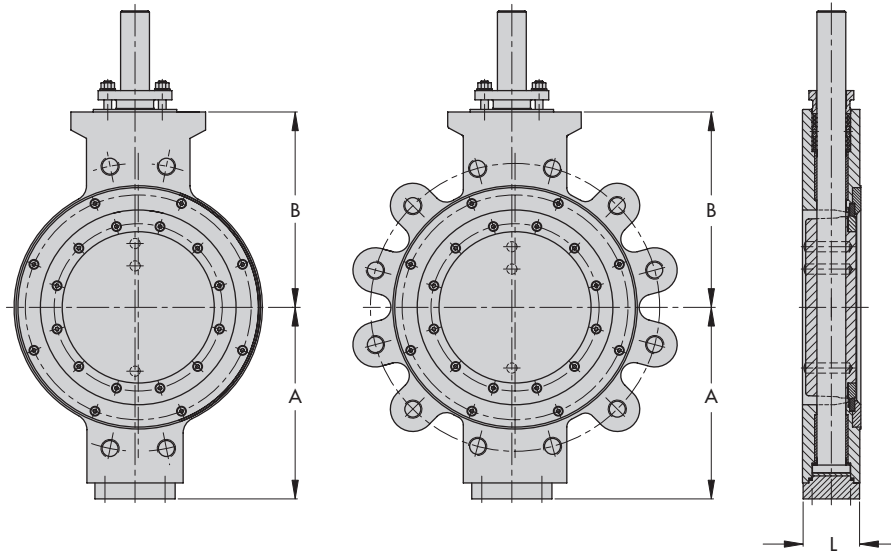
· Maßbilder für Zwischenflansch und Lug-Type-Gehäuse
